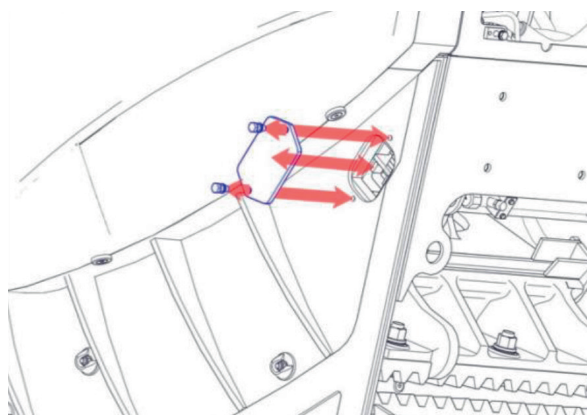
Регулировка зазора: ослабить натяжение пружины. Ослабить фиксирующий стержень и пружины. Пружины должны свободно перемещаться.
